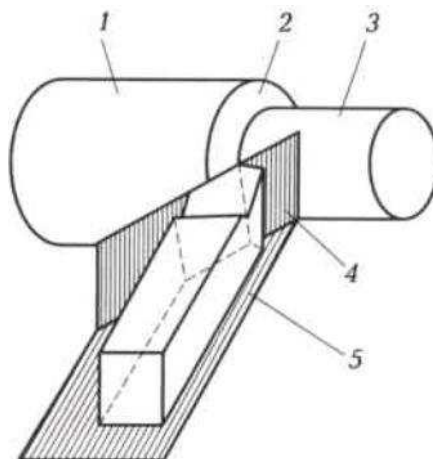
Поверхности заготовки, образуемые при обработке резцом:
